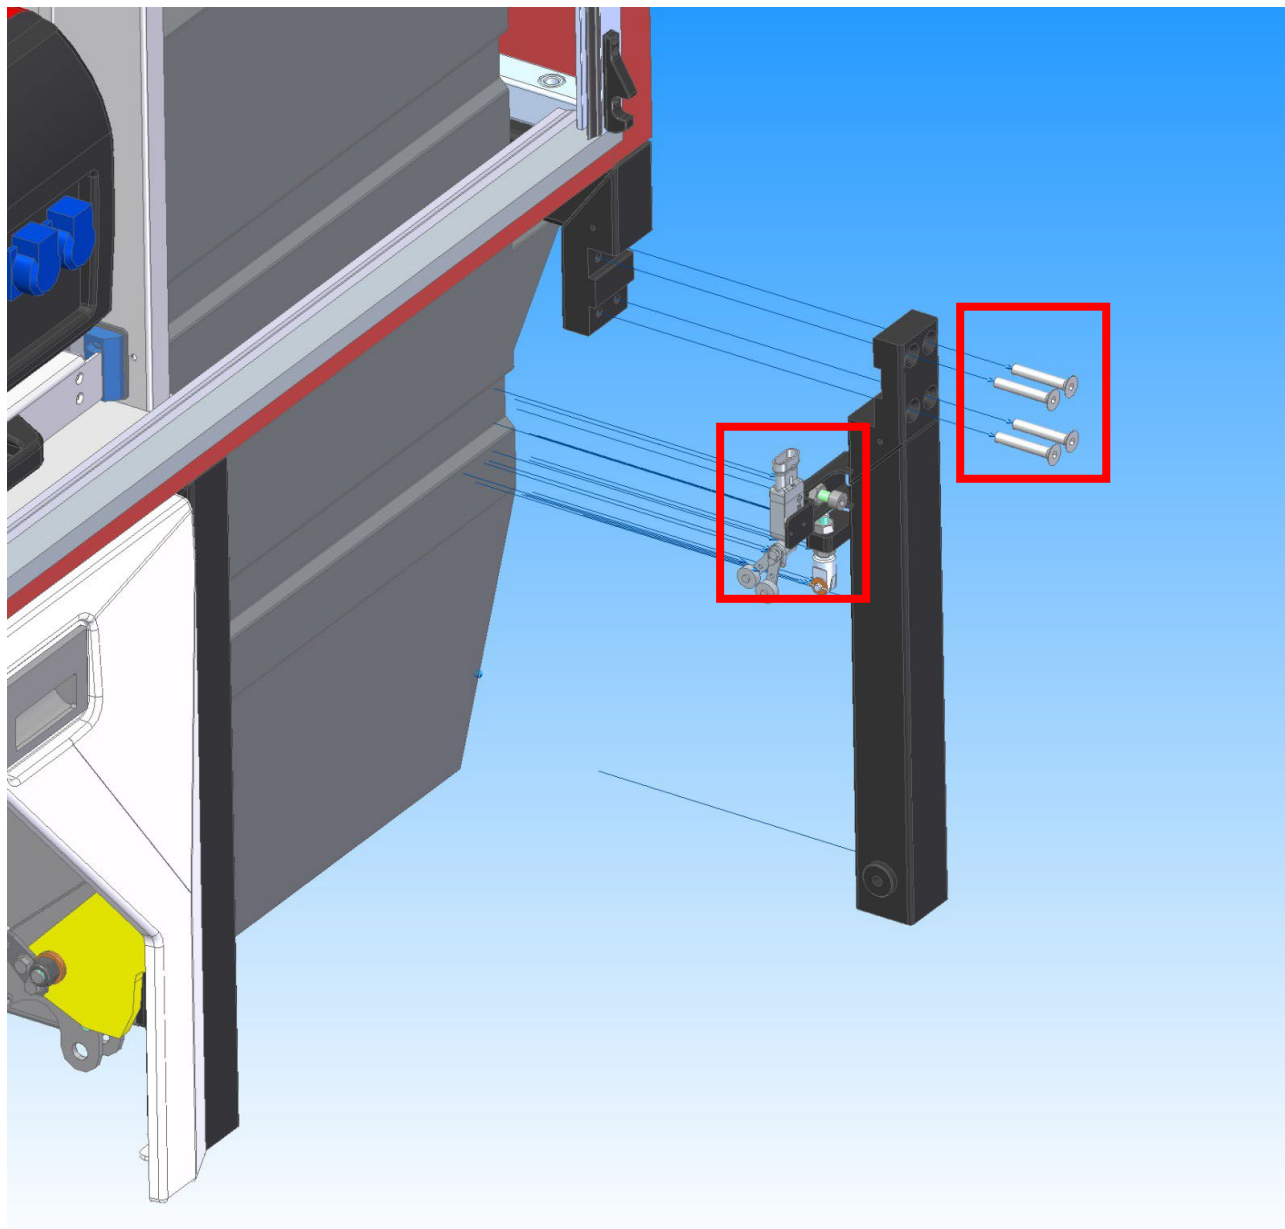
Rimozione collegamenti sensore e viti di fissaggio
